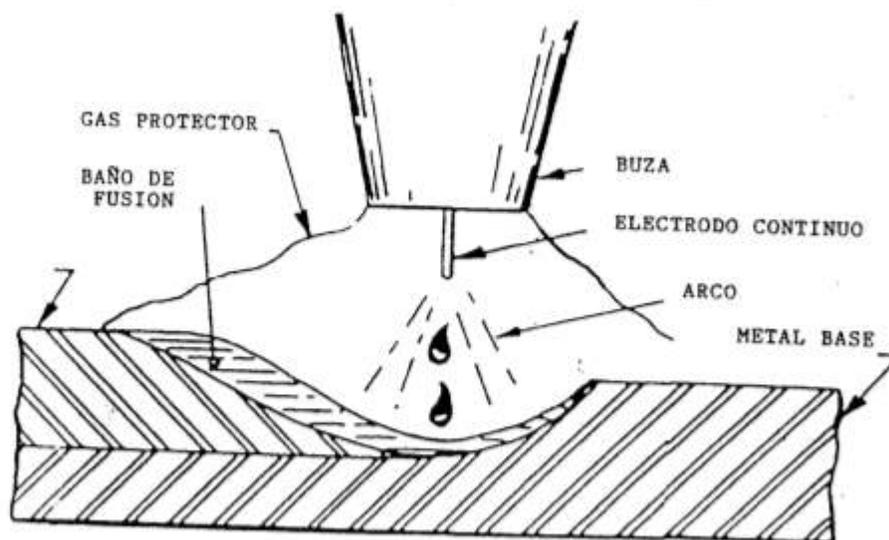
Elementos importantes soldadura MIG/MAG (SUNARC, 2007)
